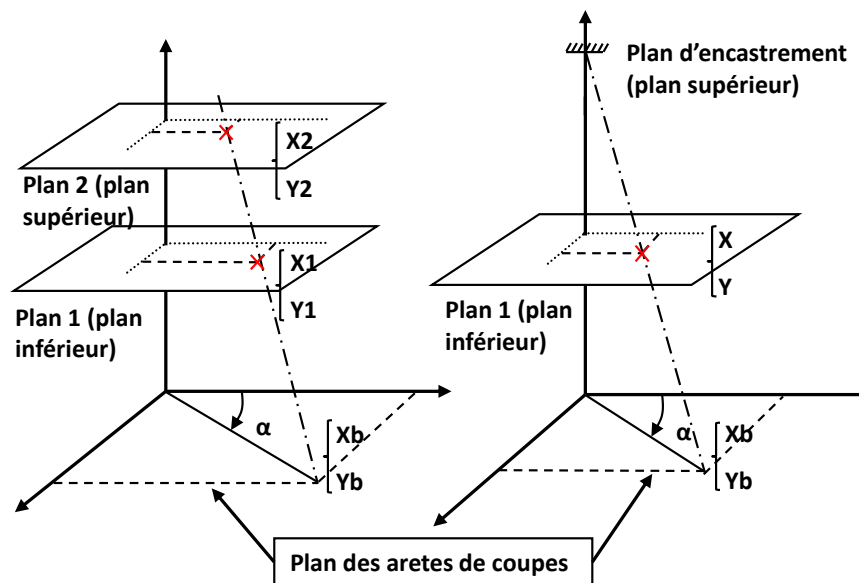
Calcul de la flexion réelle de l'outil. Avec deux plans de mesure (gauche) et avec un seul plan de mesure (droite).
